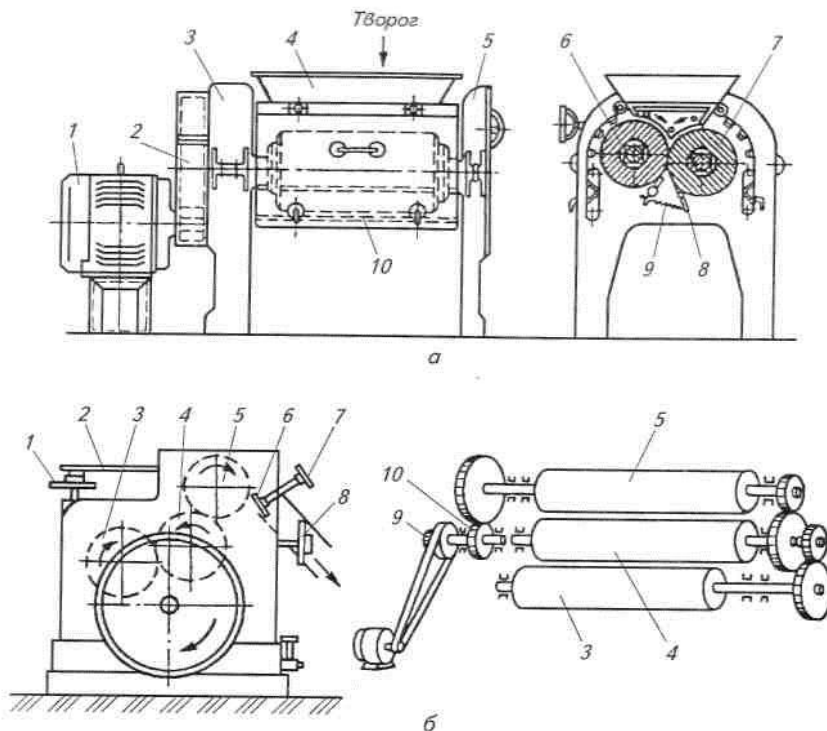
Вальцовки: а — с двумя вальцами: 1 — привод; 2 — кожух; 3, 5 — стойки; 4 — бункер; 6, 7 — вальцы; 8 — нож; 9 — пружина; 10 — стяжка; б — с тремя вальцами: 1, 8 — регулировочные винты; 2 — бункер; 3, 4, 5 — вальцы соответственно нижний, средний и верхний; 6 — нож; 7 — нажимные винты; 9, 10 — приводы
